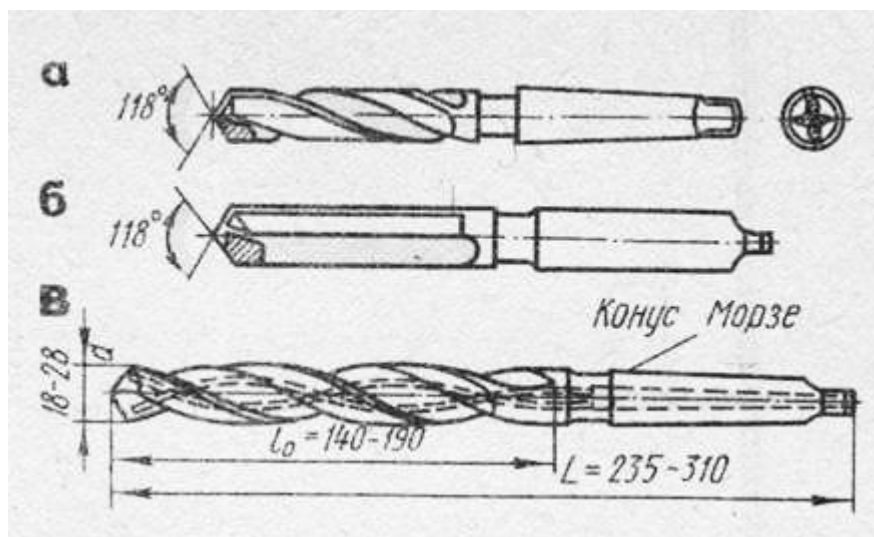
Свердла, оснащені пластинками з твердого сплаву з гвинтовими (а), прямими (б) канавками, каналами для охолоджуючої рідини (в)
